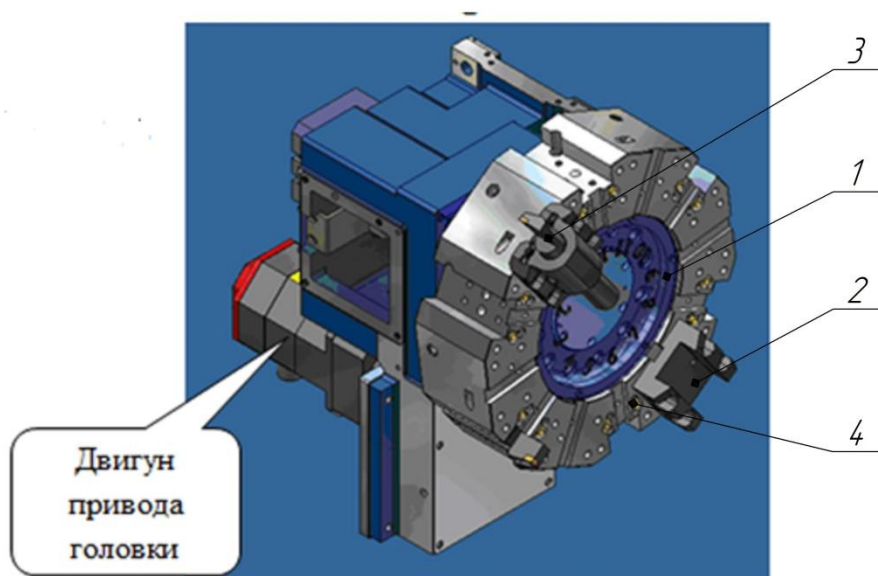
Револьверна головка з двигуном приводу головки:
